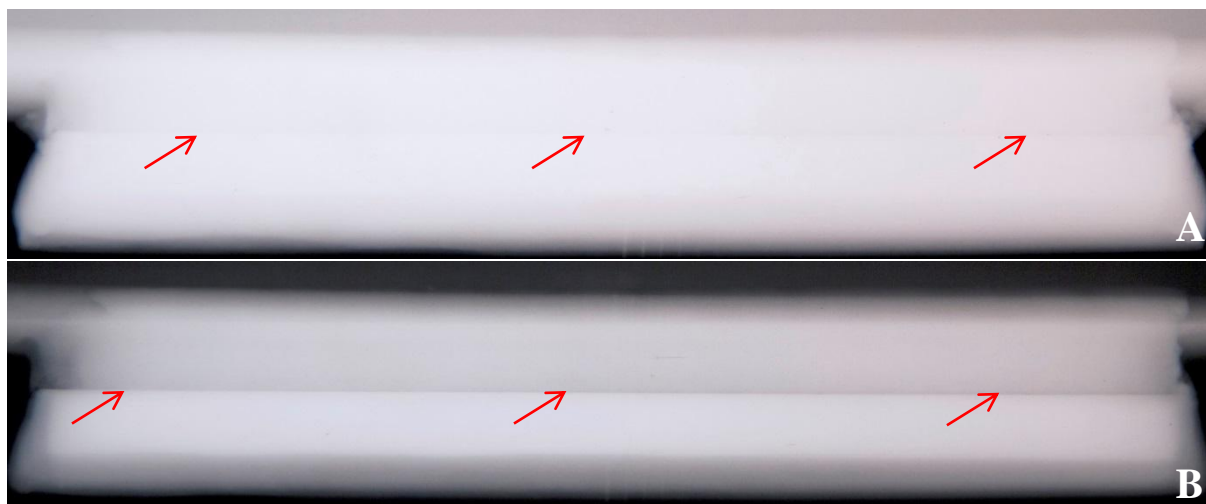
Radiografias do corpo de prova soldado com o processo RMD na posição horizontal
